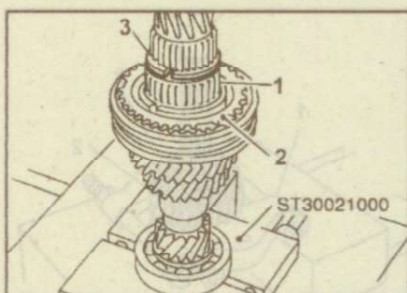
Установка игольчатого подшипника (1) шестерни 4-й передачи, блокирующего кольца (2) шестерни 4-й передачи и передних полуколец (3) шестерни 5-й передачи
